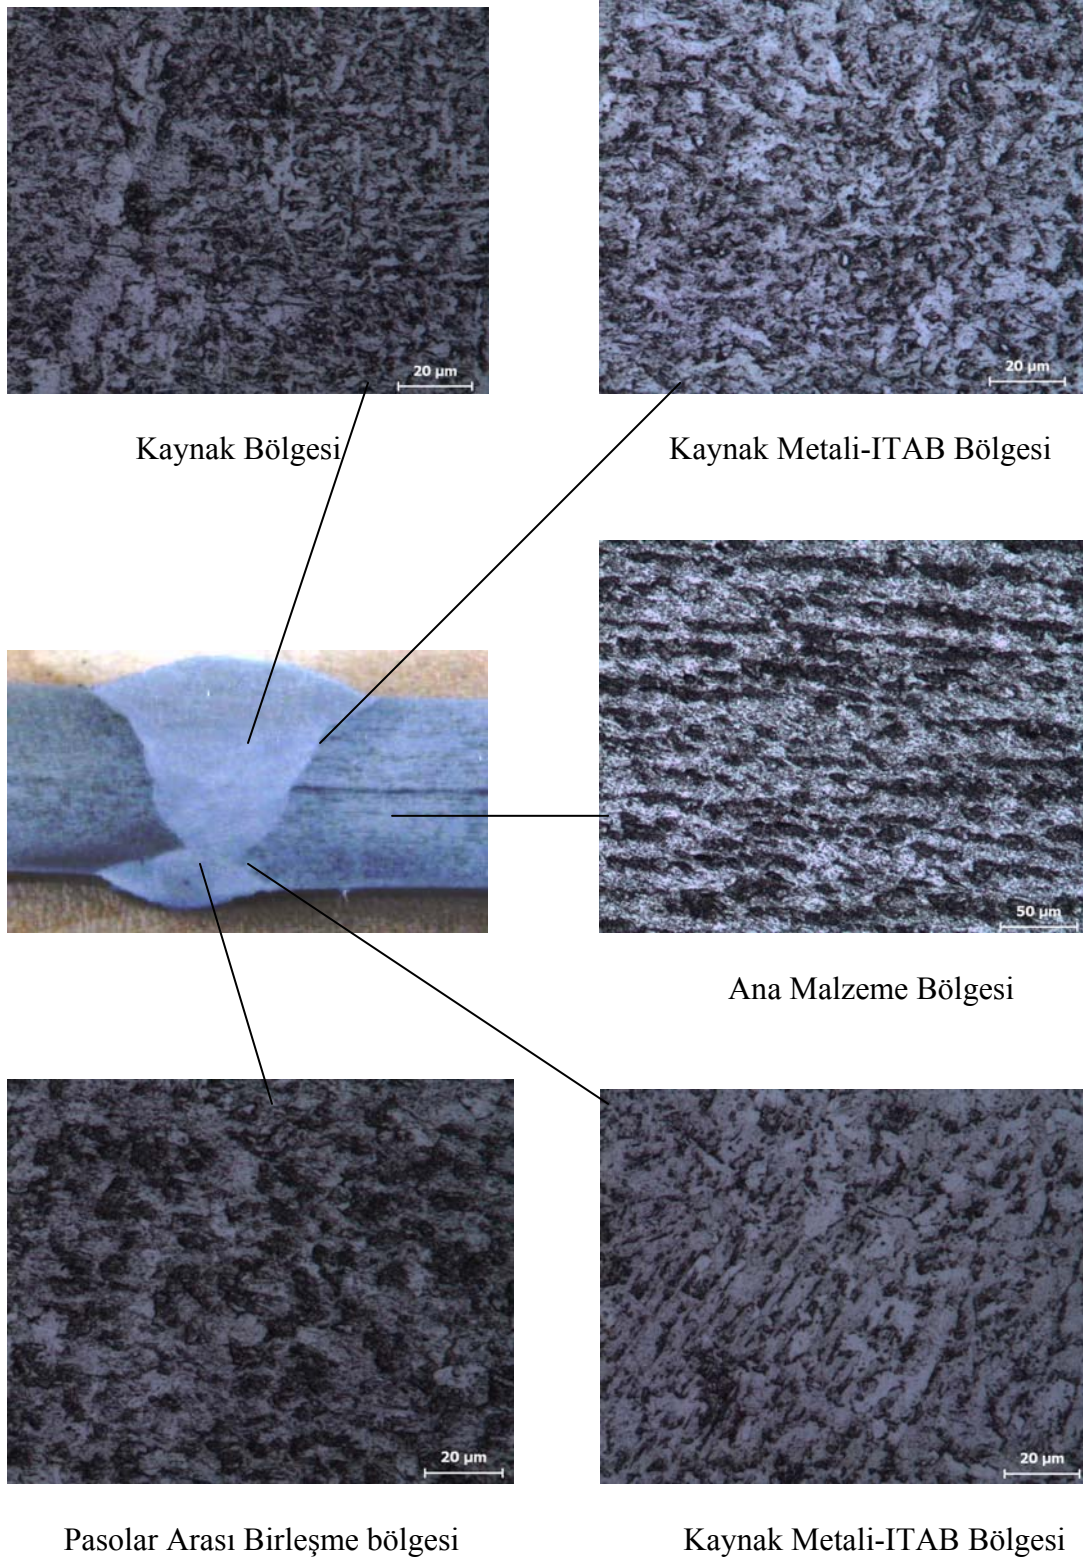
(Devam) Test parçalarının kaynak damla geometri fotoğrafları
